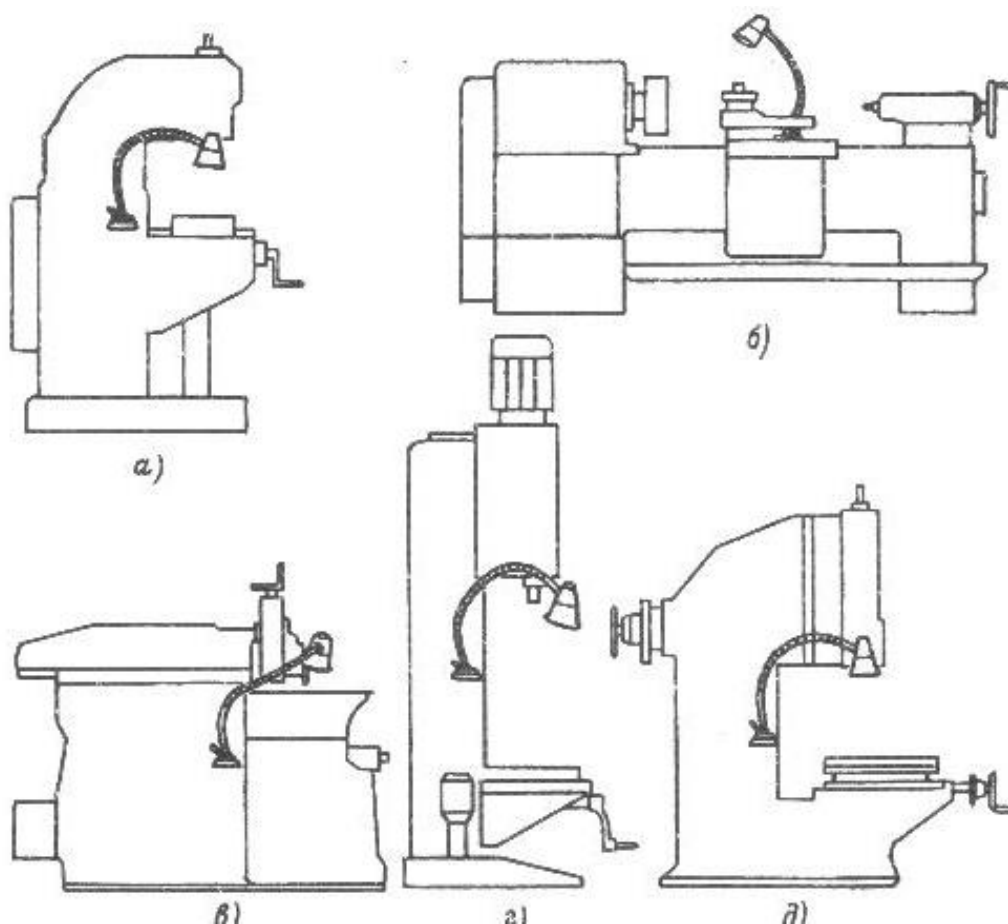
Схеми установки ОП місцевого освітлення на металообробних станках: а) вертикально-фрезерному; б) токарному; в) поперечно-строгальному; г) свердлильному; д) довбальному.
